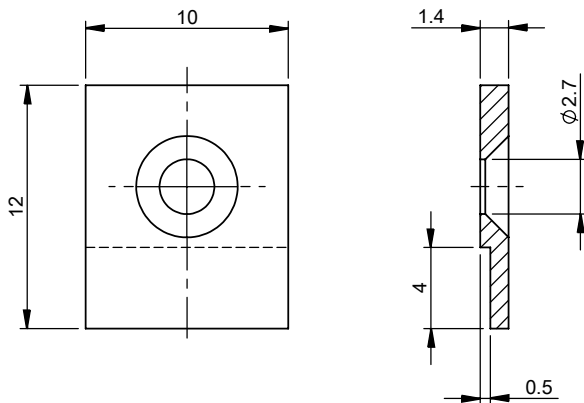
Fermo BAM MC-ML-062-001-4
